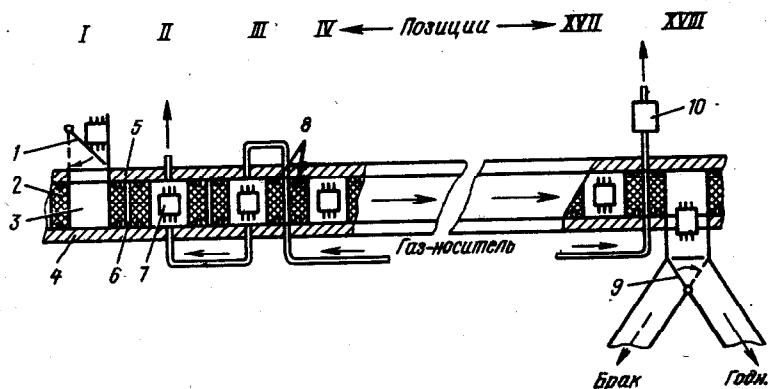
Схема устройства узла проверки полуавтомата 12ГАЗ-1000-004 с электрозахватным датчиком разбраковки изделий
